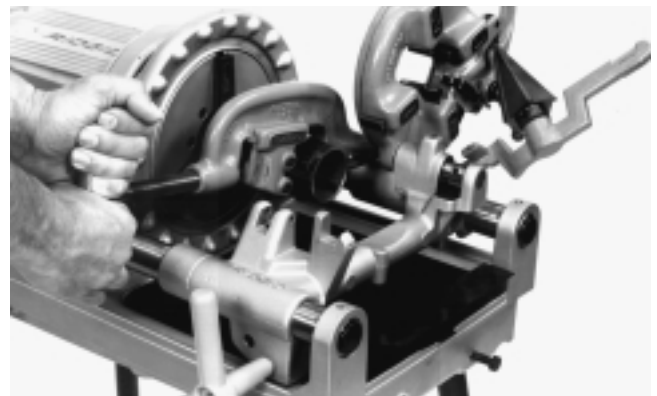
Coupe des tuyaux à l'aide de la machine à fileter 300 Compact
